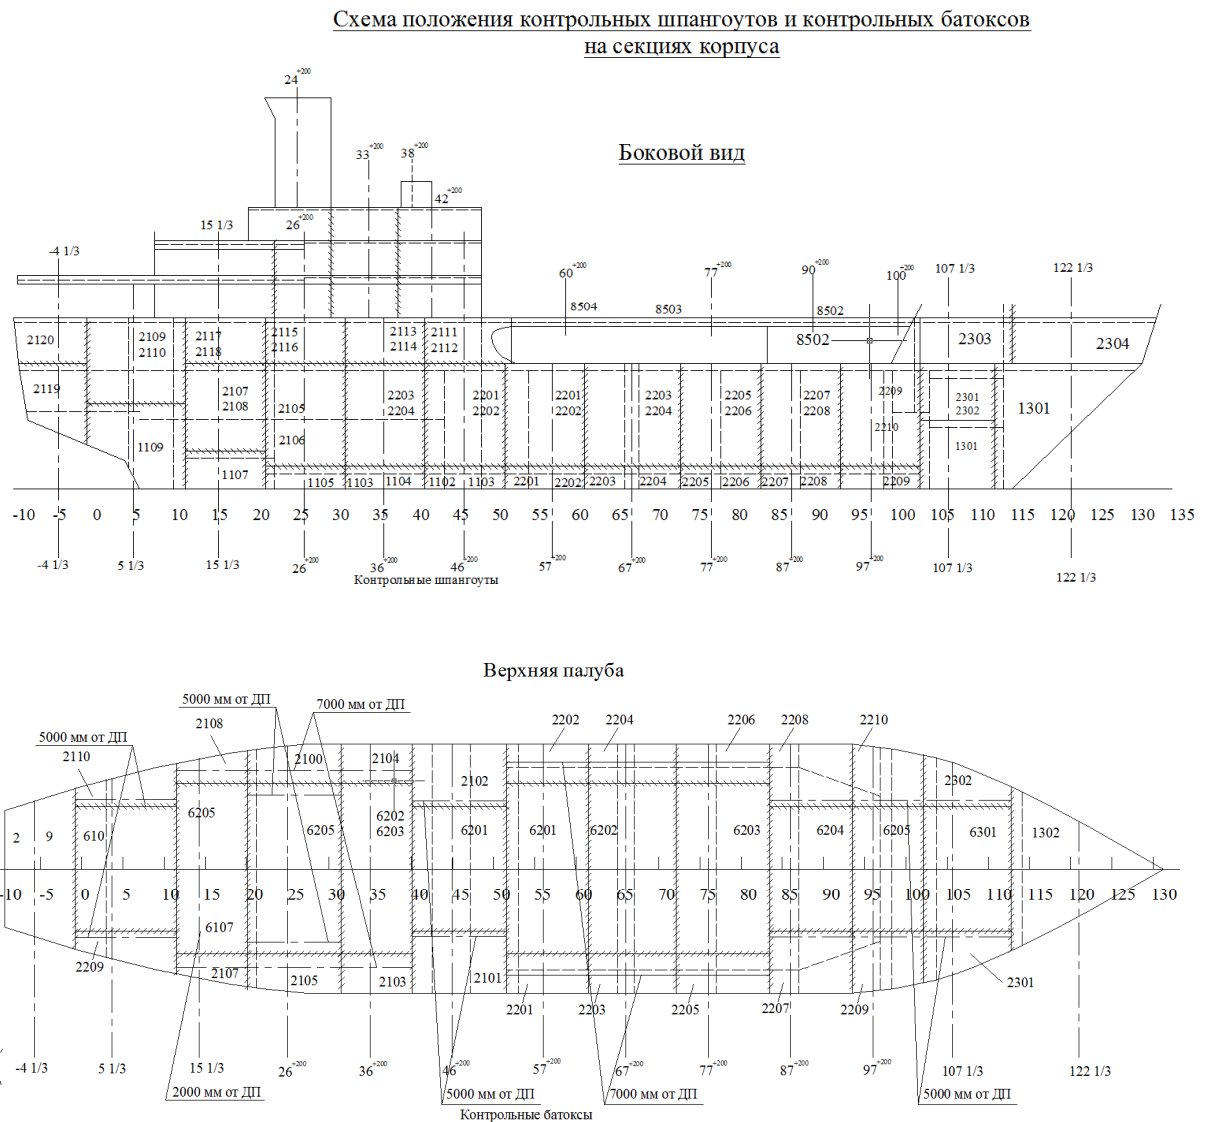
Пример выполнения чертежа разбивки корпуса на сборочные единицы
